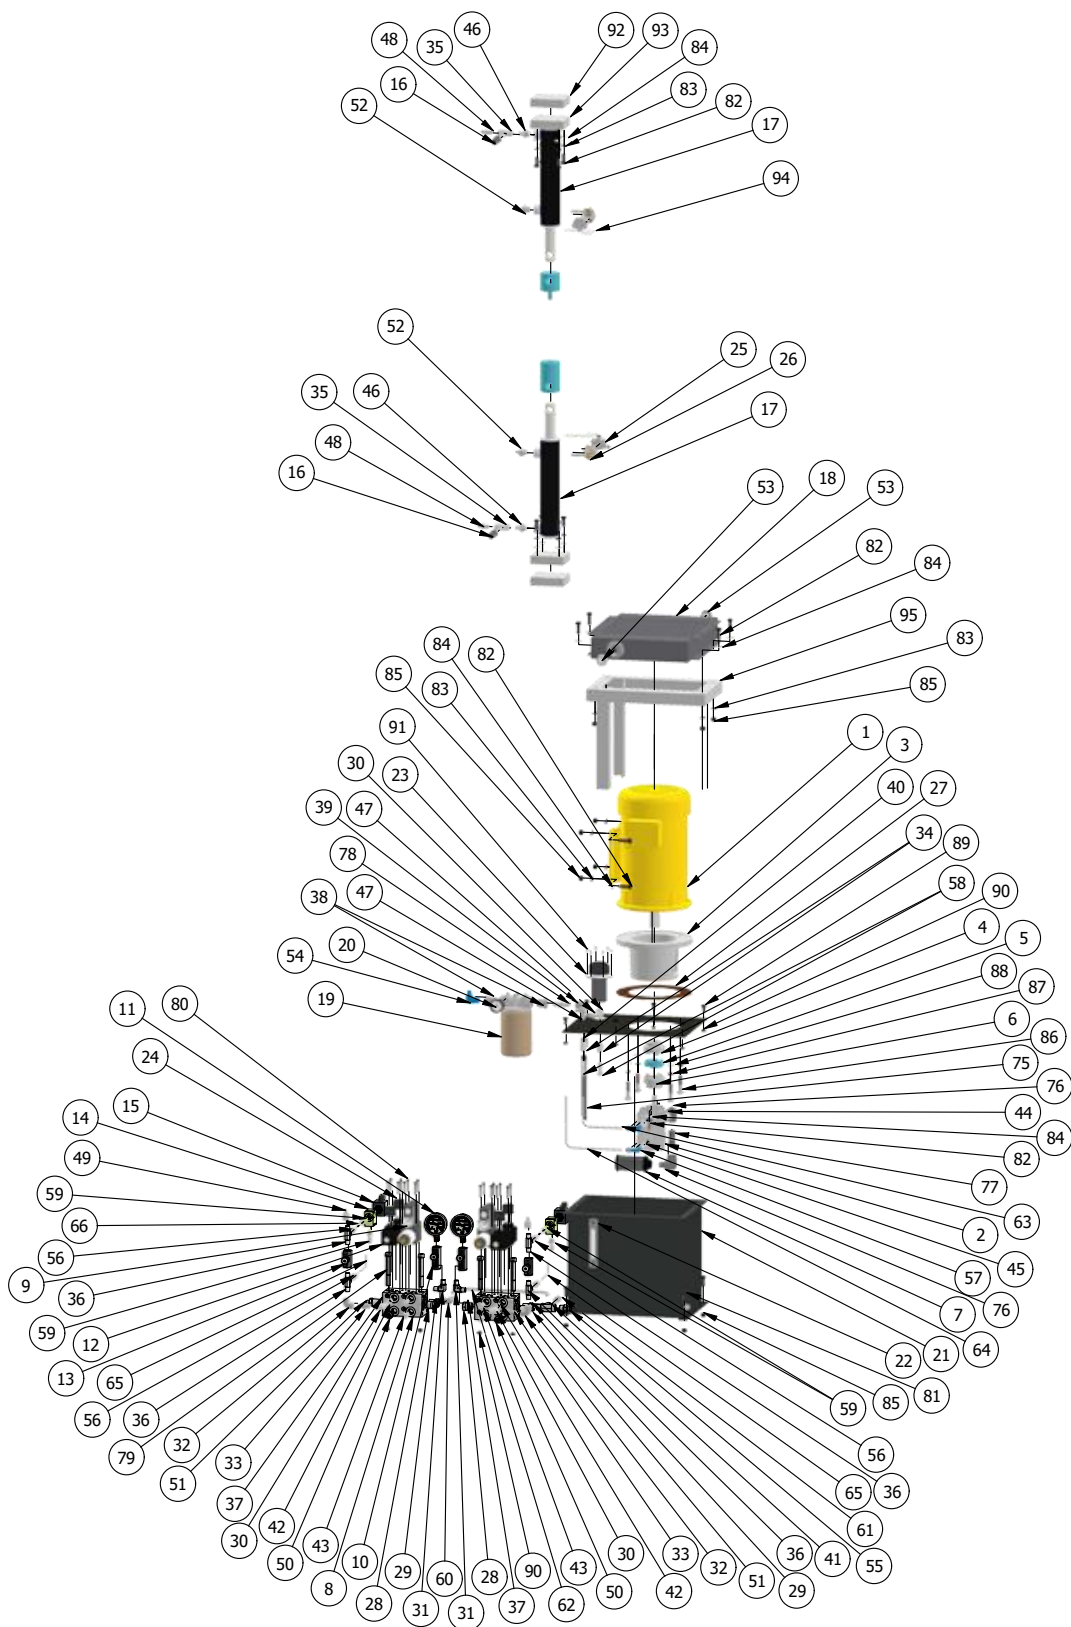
Dibujo explosionado de componentes internos de la prensa.
